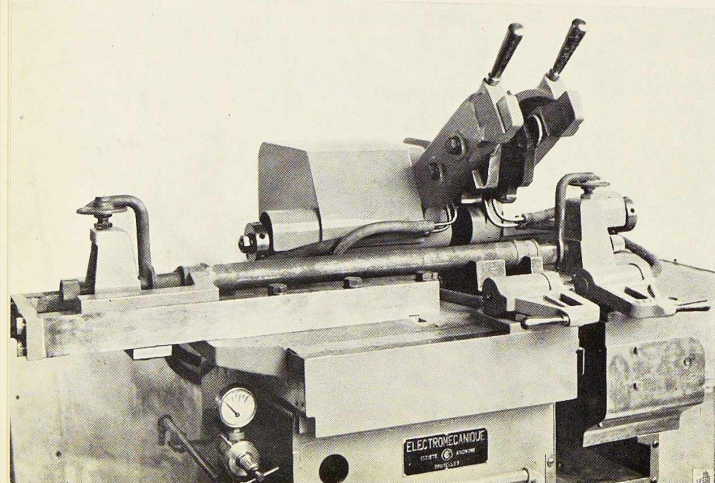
Disposition des pièces pour la réalisation de la première et de la deuxième soudures.
